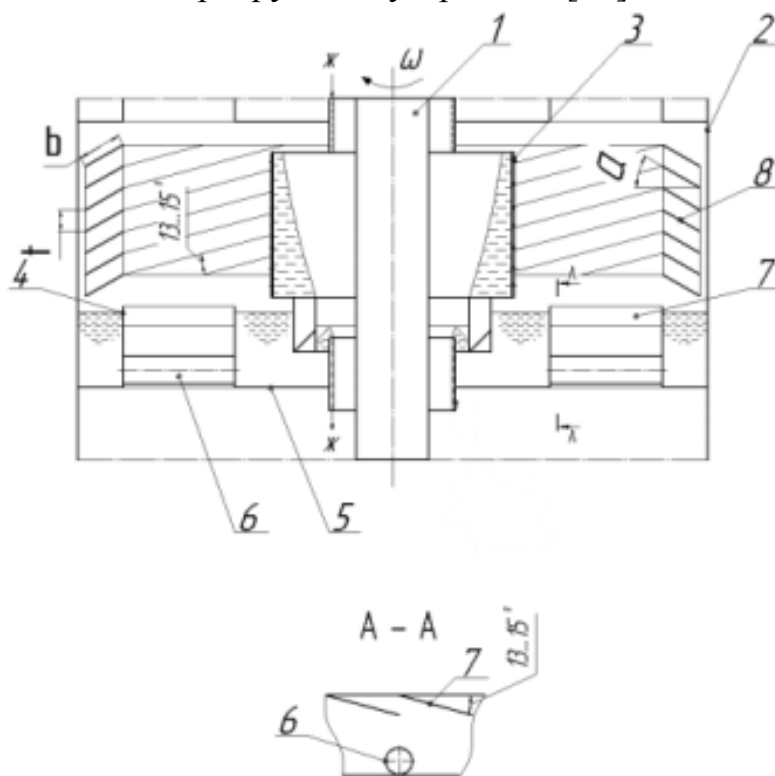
Схема исследуемой конструкции КЭ: 1 - вал; 2 - корпус; 3 - диспергирующее устройство; 4 - газоходы; 5 - сливная тарелка; 6 - переточные трубы; 7 - направляющие лопатки; 8 - пристенный каплеотбойник
